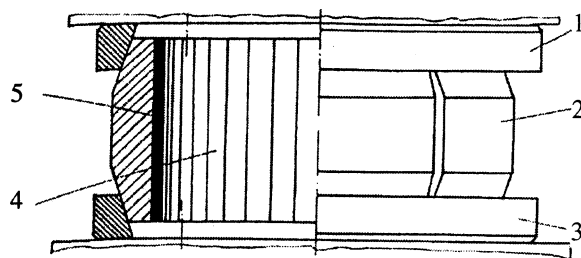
Схема секторной пресс-формы для изготовления зубчатых ремней
